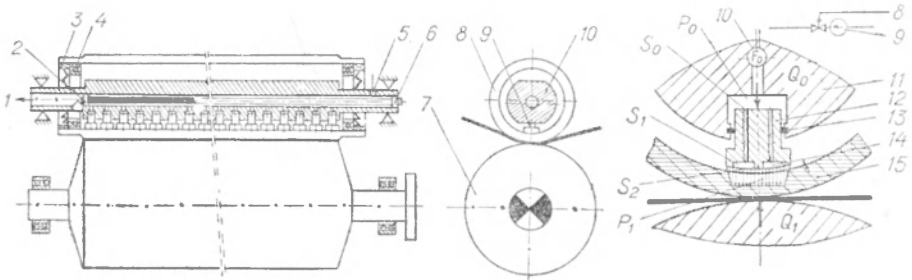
Конструкція друкарського циліндра «Nipco-Print»:
